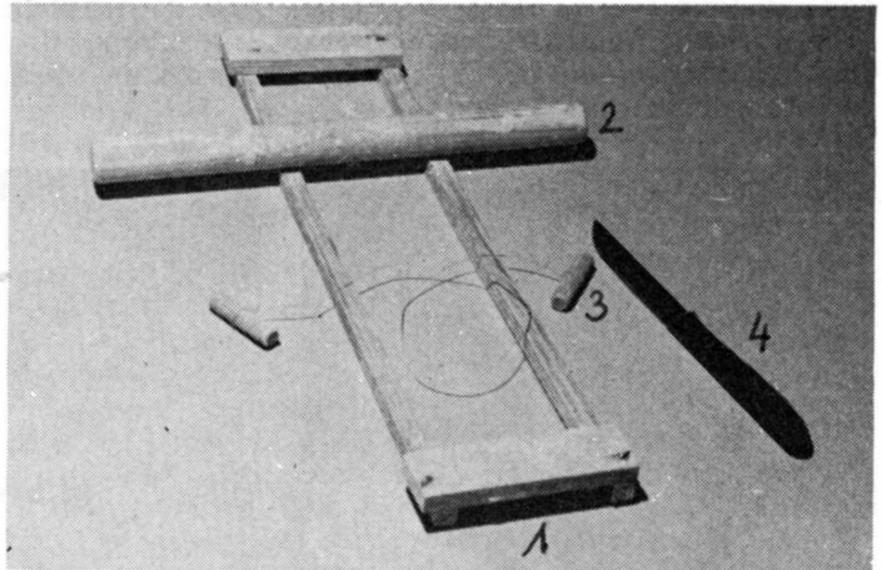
Werkzeuge für die Plattentechnik: (1) Distanzholz (2) Rundholz (3) Tonschneider (4) Schneidmesser
